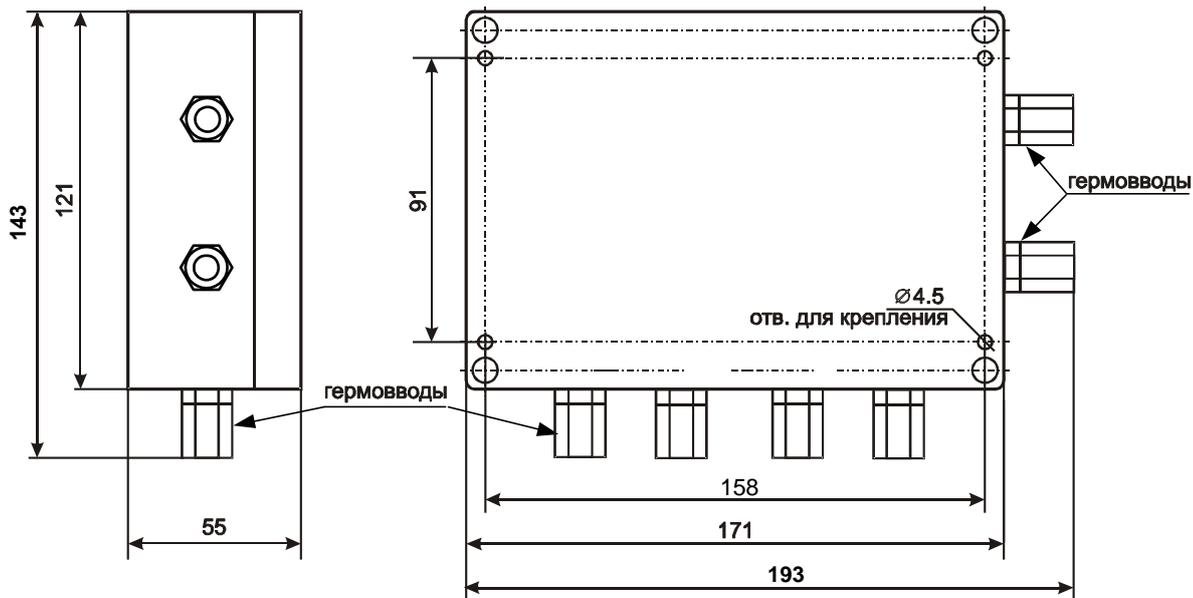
Габаритные и присоединительные размеры (исп. IP65)
